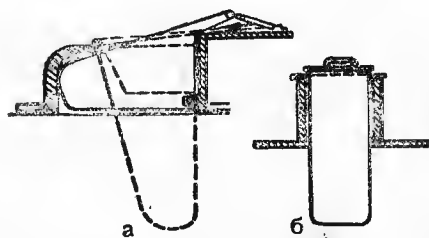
Виды швертов: а — поворачивающийся шверт в поднятом и опущенном состоянии, б — кинжальный шверт.
